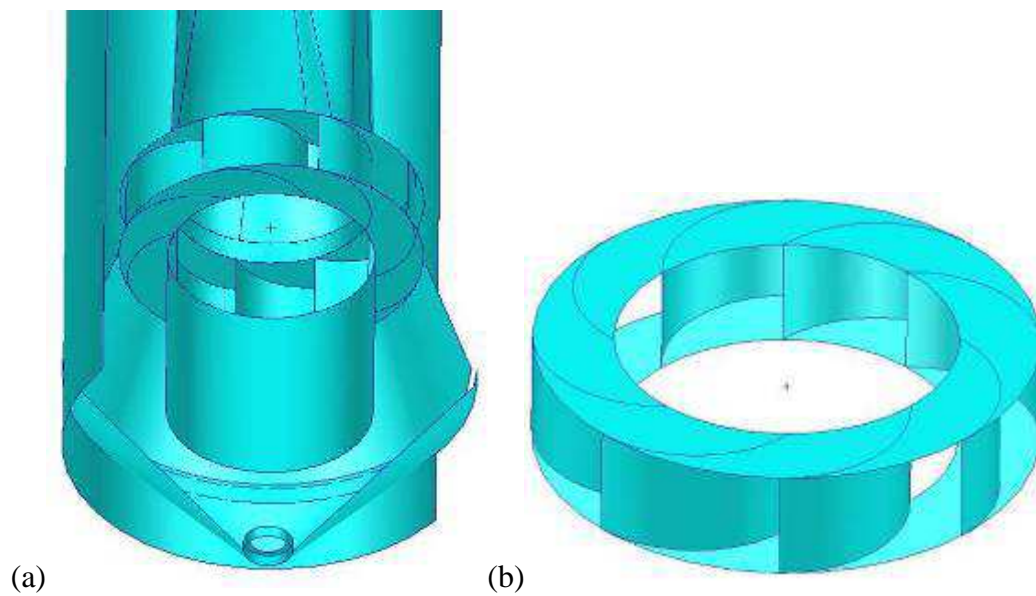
Geometria Original - (a) Vista Interna em Corte e (b) Vista Interna do Rotor
